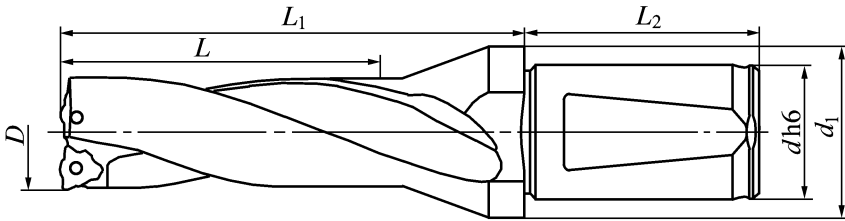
Сверла со сменными пластинами "DRDRILLS"
